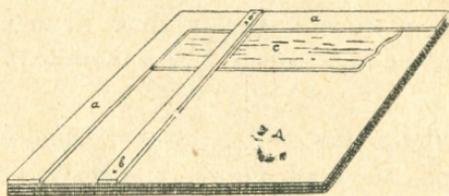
Приспособление для резки одинакового размера диапозитивных стёкол.
